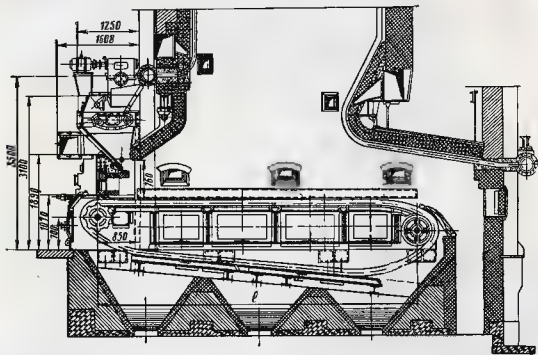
Двухступенчатая толка «ВТИ-Комега-УЦР»
